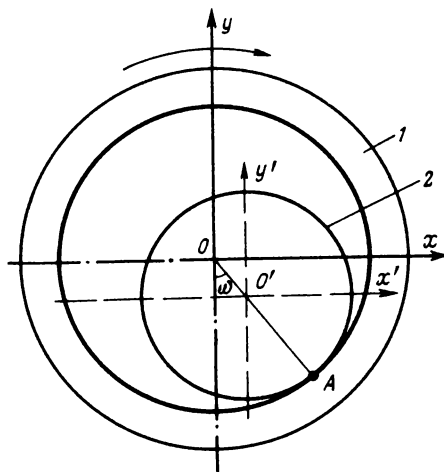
Схема смещения центра поперечного сечения корпуса вращающейся печи относительно бандажа:
